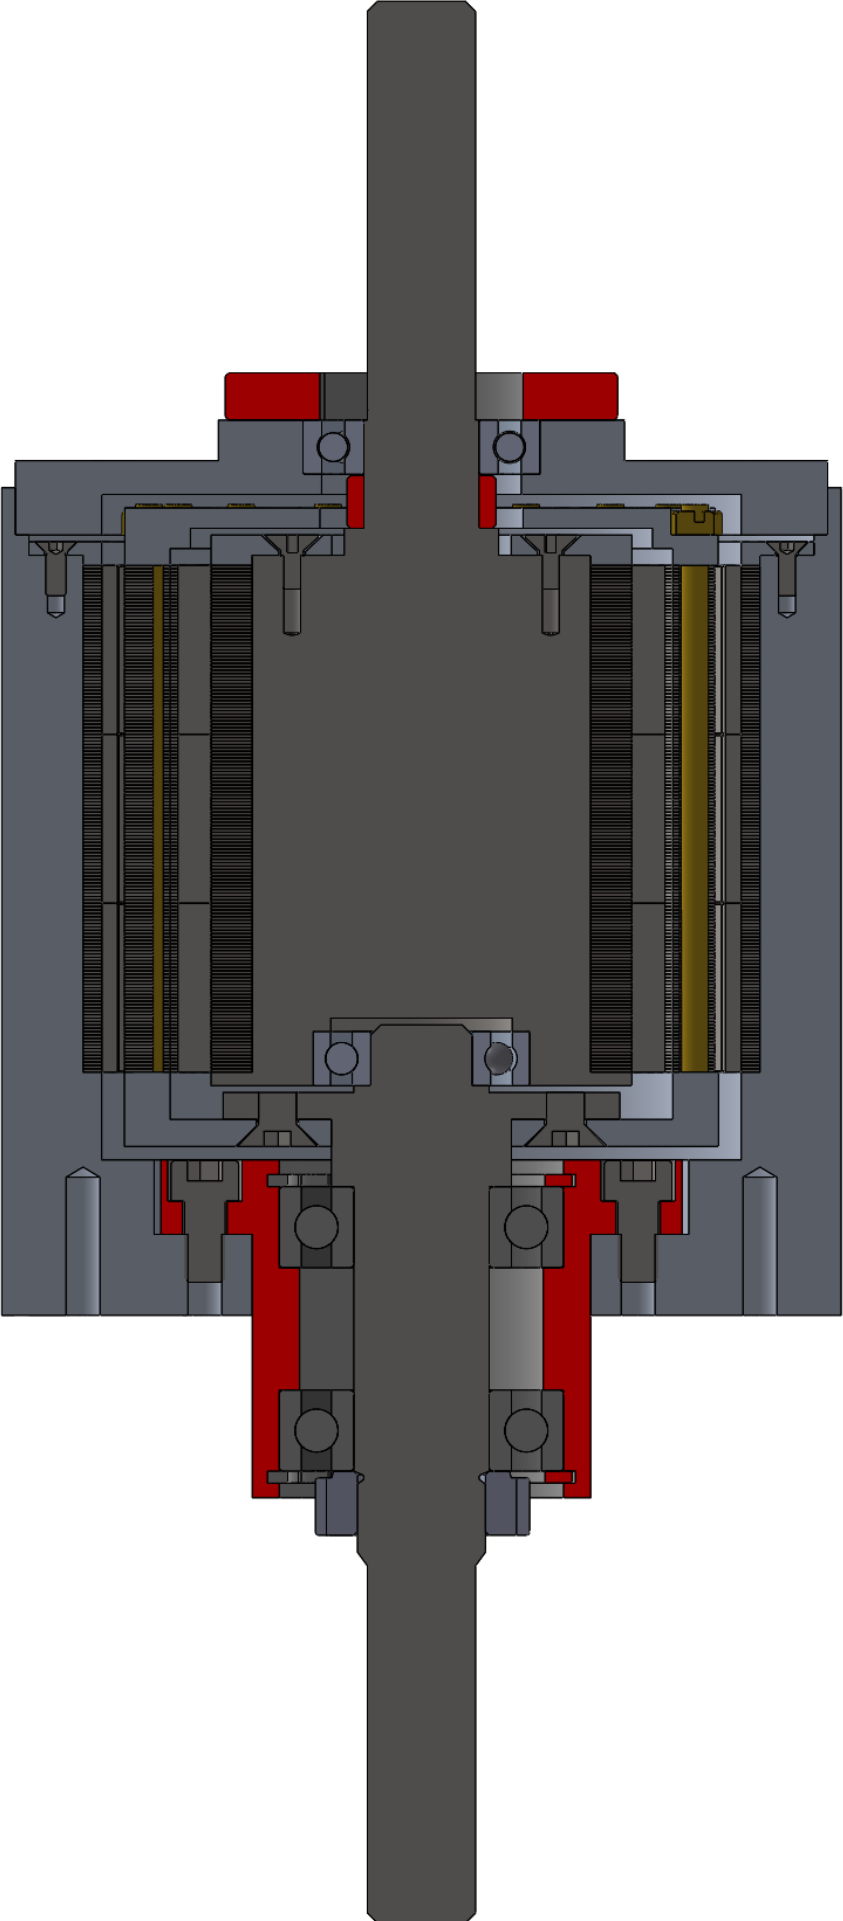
Coupe du modèle 3D du prototype final
